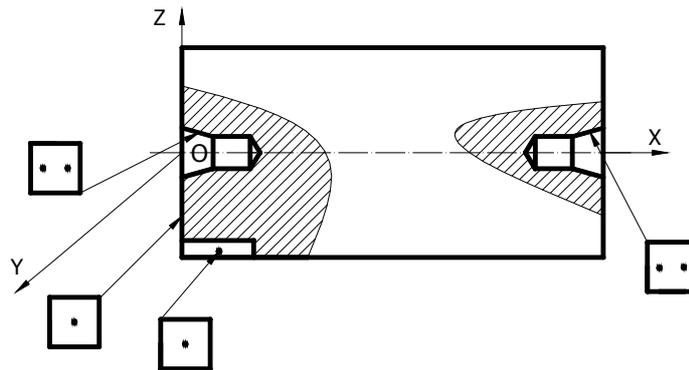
Схема установки детали на передний плавающий и задний жесткий центры.
